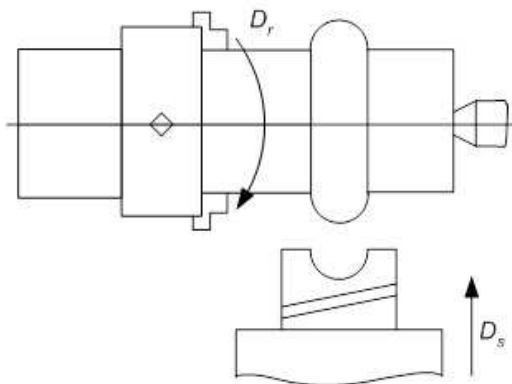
Схема получения образующей конуса широким резцом
